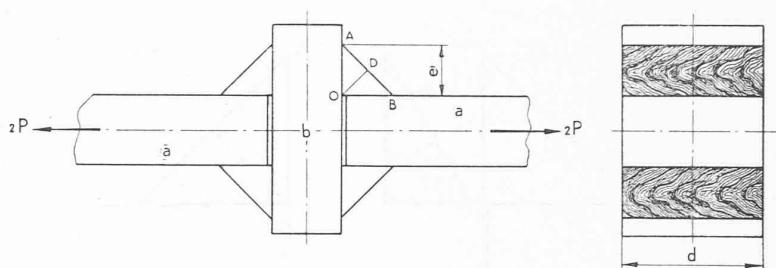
Assemblage soudé sans recouvrement.
